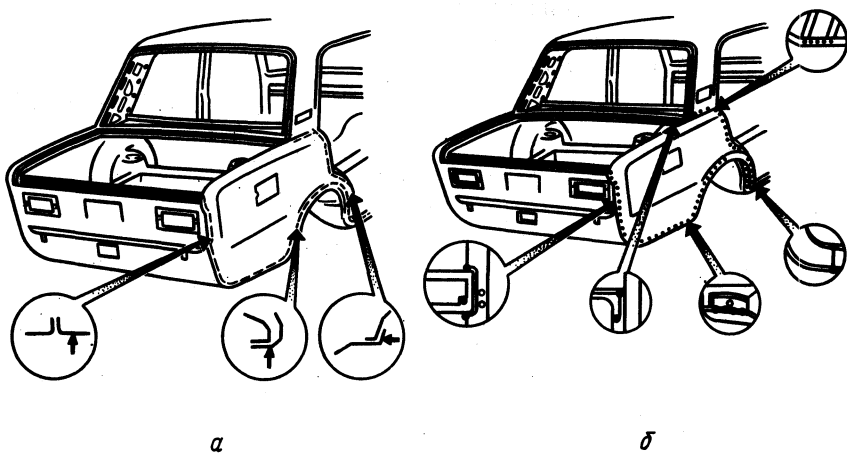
Замена заднего крыла автомобиля «Жигули»: а — места и линии рубки крыла; б — точки сварки крыла
